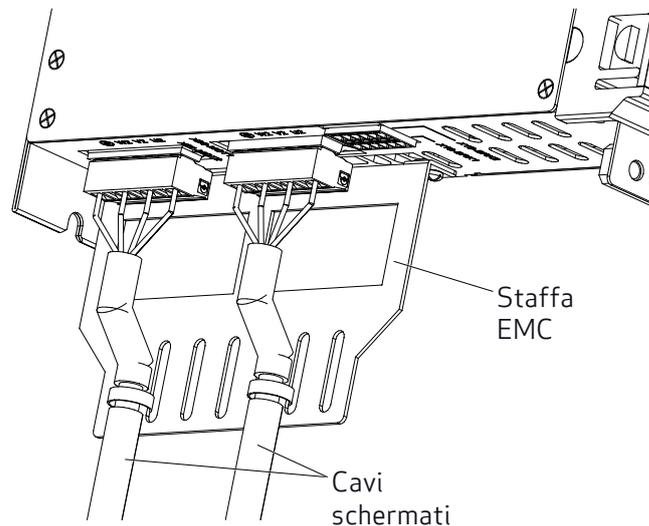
Dettaglio di collegamento Cavi-Staffa EMC
